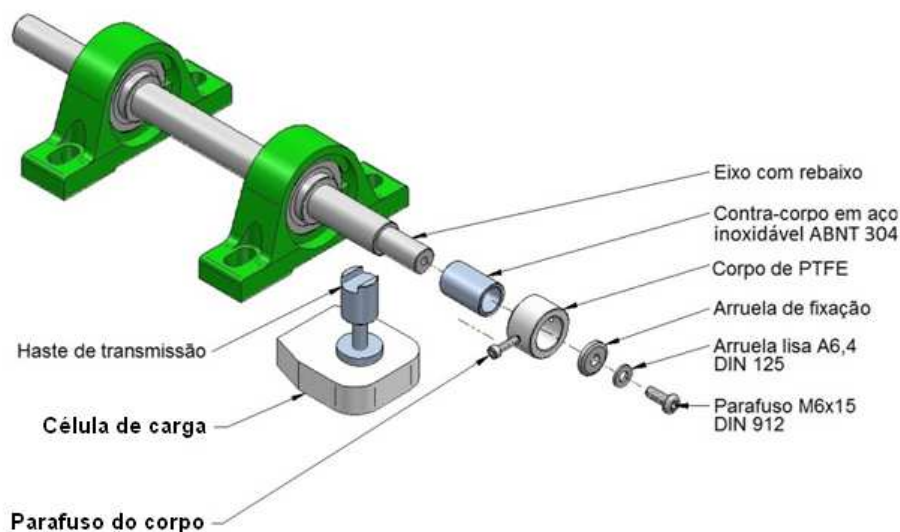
Vista explodida da montagem do corpo e contra-corpo na MAC.
